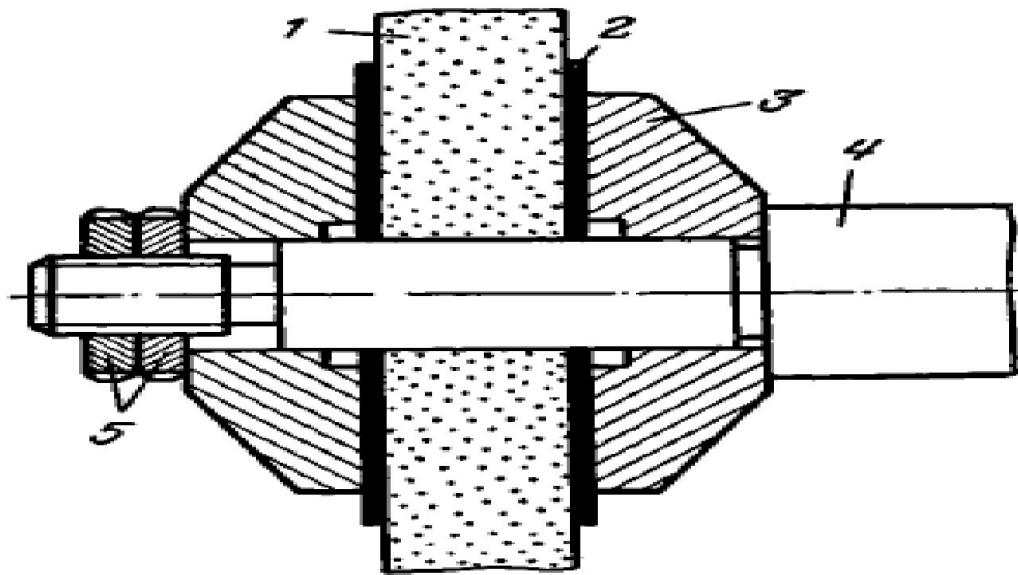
Схема крепления заточного круга на шпинделе заточного станка
